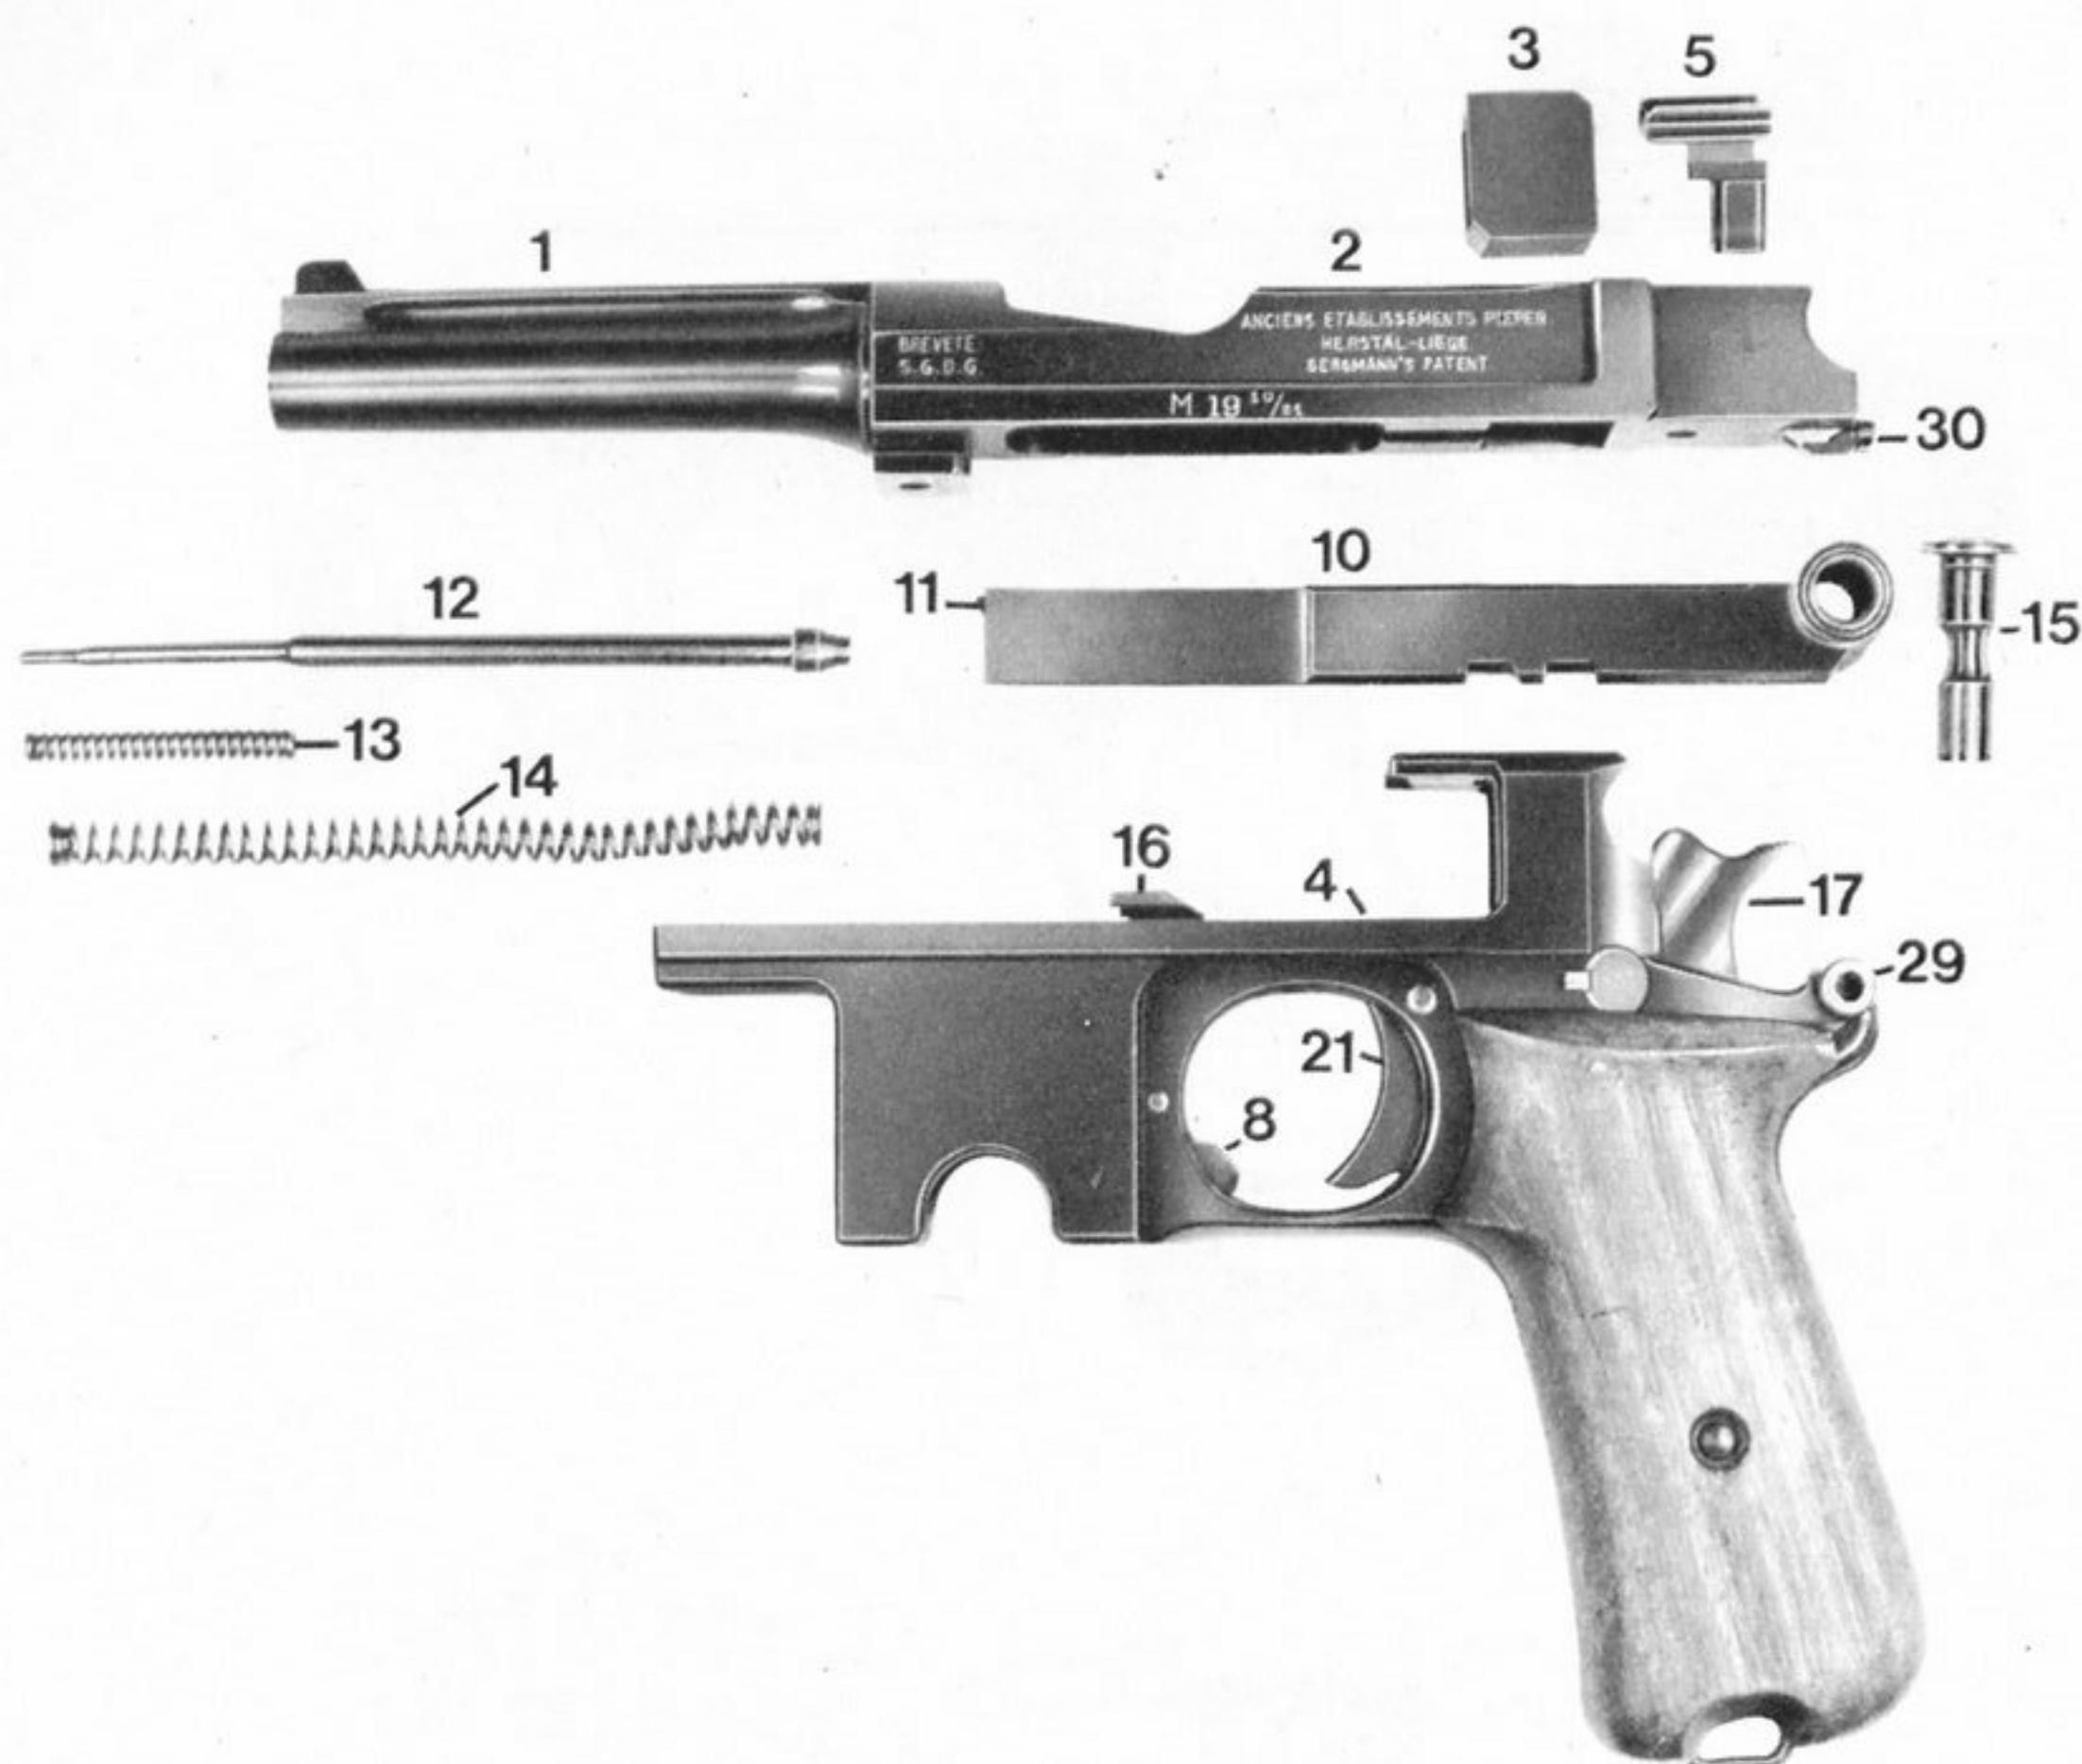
Pistole zerlegt: 1 = Lauf, 2 = Schlitten, 3 = Verriegelungsstück, 4 = Griffstück, 5 = Kimmenstück, 8 = Magazinhalter, 10 = Verschußstück, 11 = Auszieher, 12 = Schlagbolzen, 13 = Schlagbolzenfeder, 14 = Schließfeder, 15 = Haltebolzen, 16 = Auswerfer, 17 = Hammer, 21 = Abzug, 29 = Sicherungshebel, 30 = Nocken
